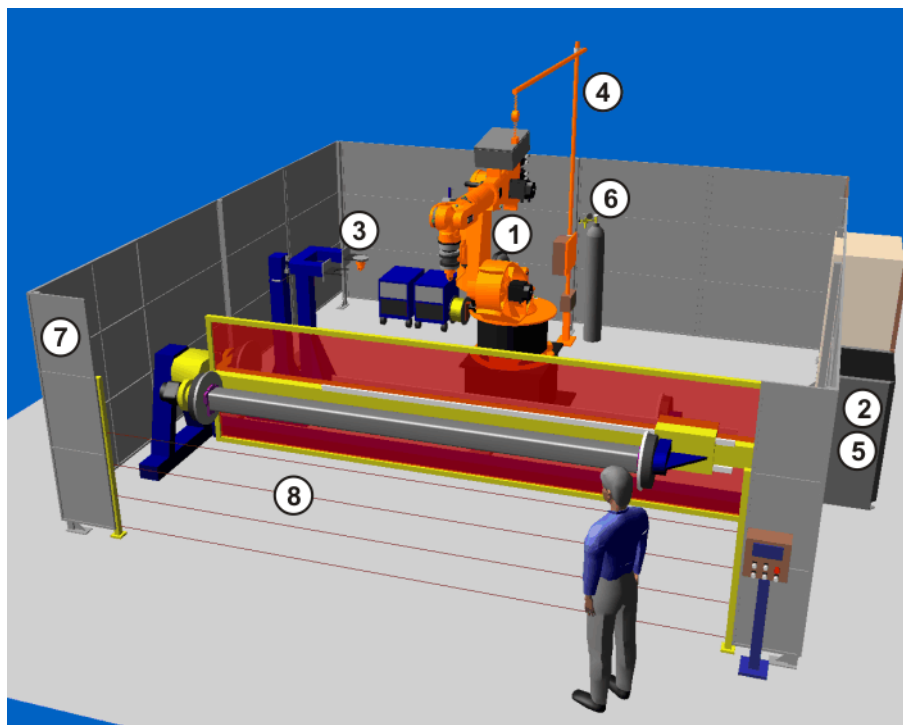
Сварная секция для сварки в среде защитного газа
